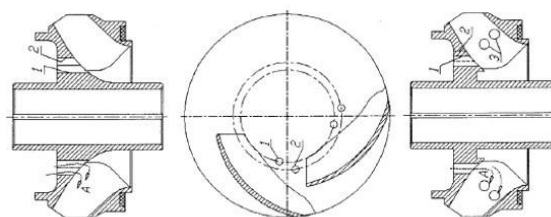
Рабочие колеса диспергатора типа AGH
